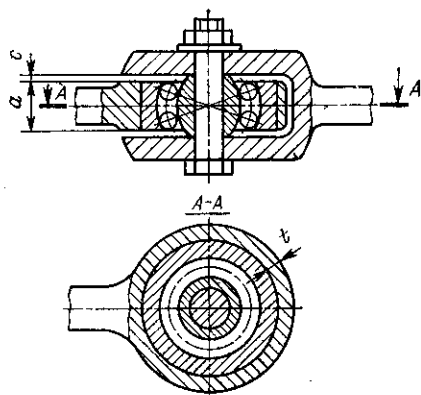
Проушина подвижного соединения с запрессованным подшипником
